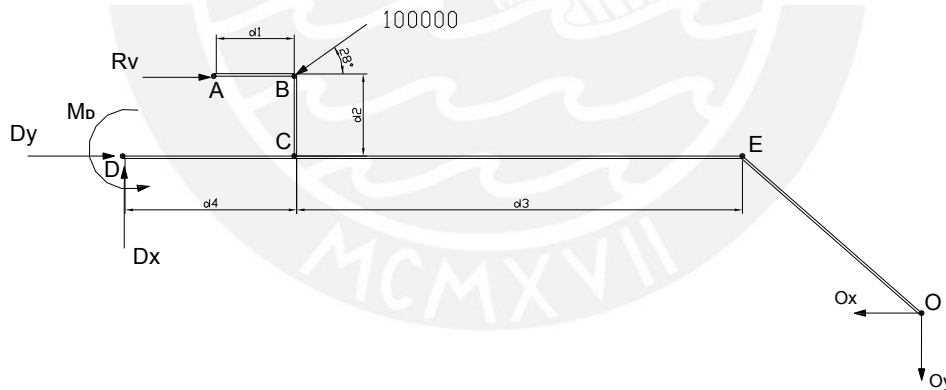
BARRA DE GIRO.D.C.L. HORIZONTAL: SECCIÓN A-A
